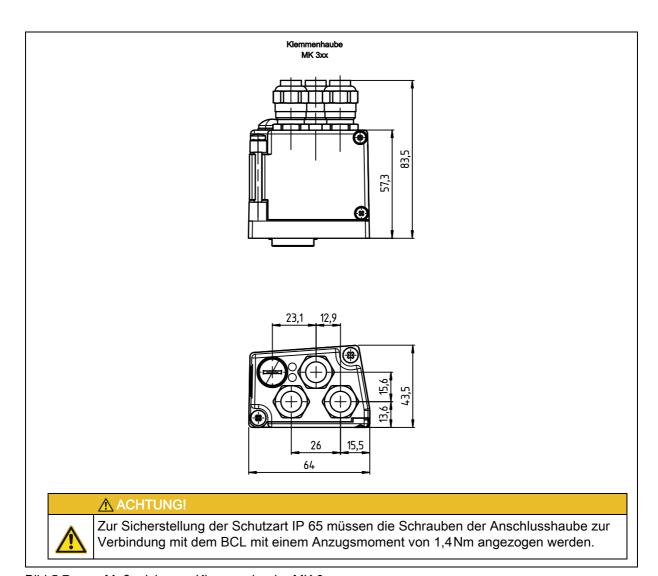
Maßzeichnung Klemmenhaube MK 3xx
